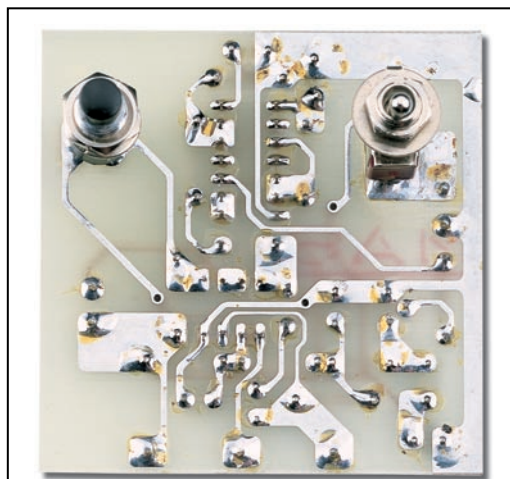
Le même circuit imprimé, vu du côté des soudures. Remarquez P1 et S1.
